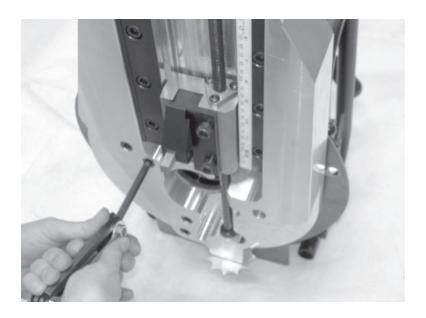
Отверните 6 шт. винтов, крепящих однорезцовый суппорт.
